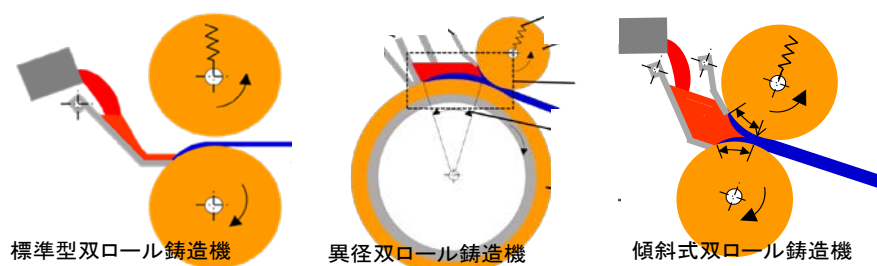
試験 casting に用いた 3 方式の双ロール casting 法
